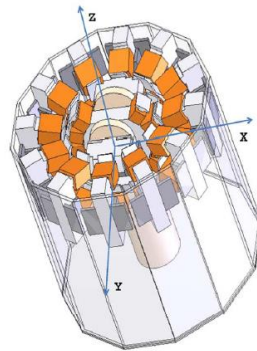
Küresel indüksiyon motorunun rotoru ve statoru [24]
